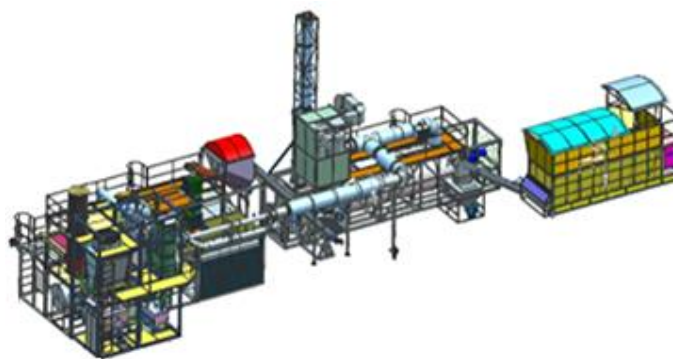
Общий вид установки быстрого пиролиза с габаритными размерами 31,5×7×9,1 [м]
